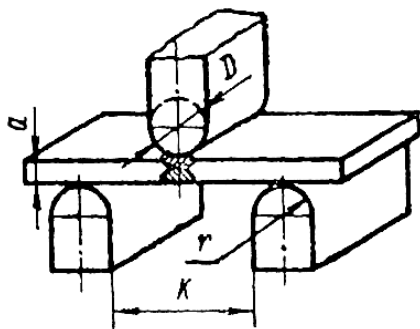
Схема испытания образцов при изгибе параллельно оси сварного шва
